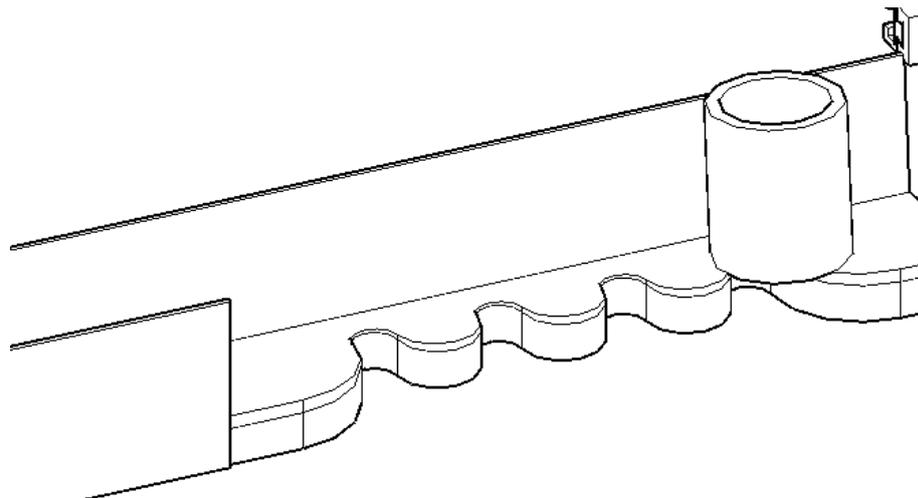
Pistón apoyado sobre su base avanzando por la tercera sección. Fuente: elaboración propia.
